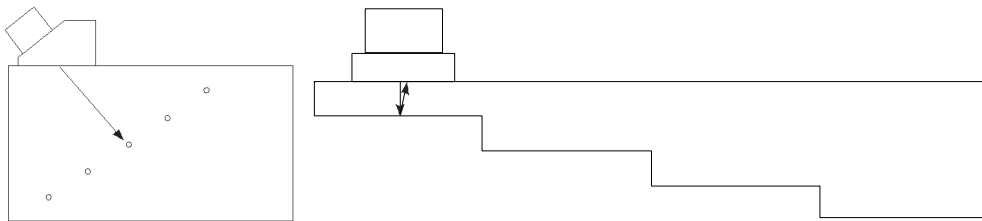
Калибровочные образцы для калибровки кривой ВРЧ
